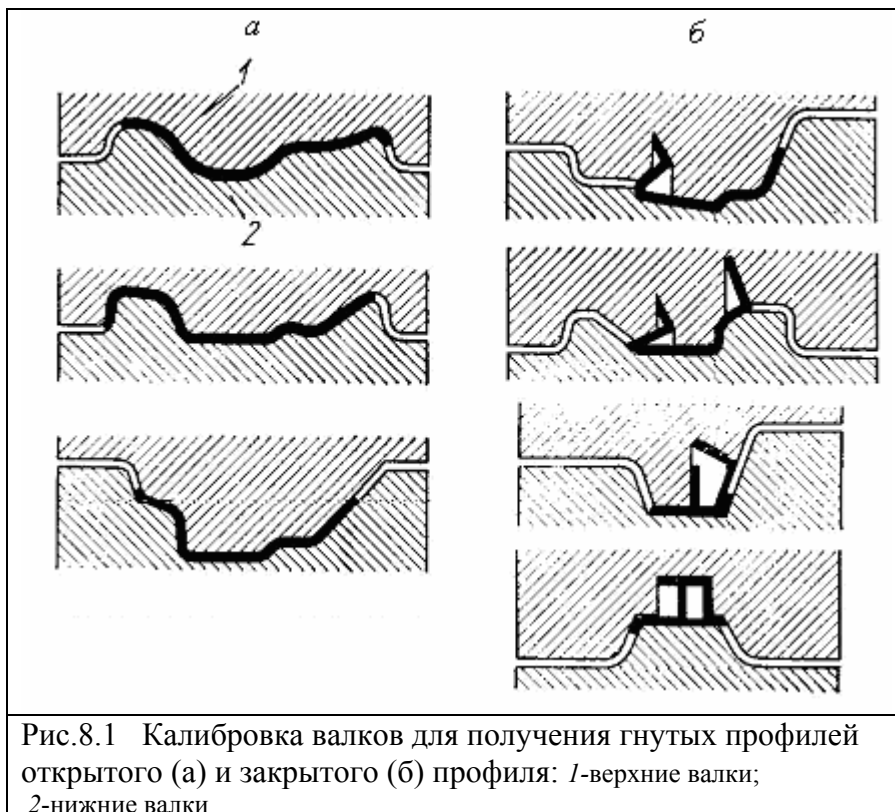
Калибровка валков для получения гнутых профилей открытого (а) и закрытого (б) профиля: 1-верхние валки; 2-нижние валки
